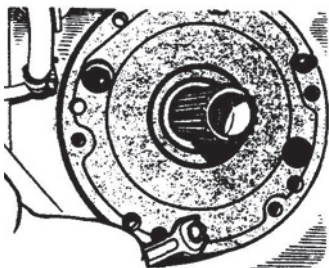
Выпрессовка крышки стакана подшипников конечной передачи, замена манжеты.
